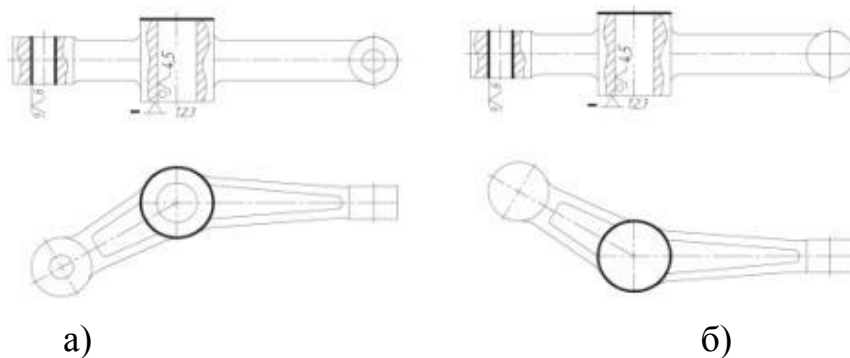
Схема базування заготовки на плоскошліфувальній 45 операції:
